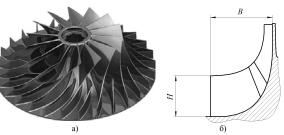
Общий вид центробежного моноколеса и эскиз лопатки
